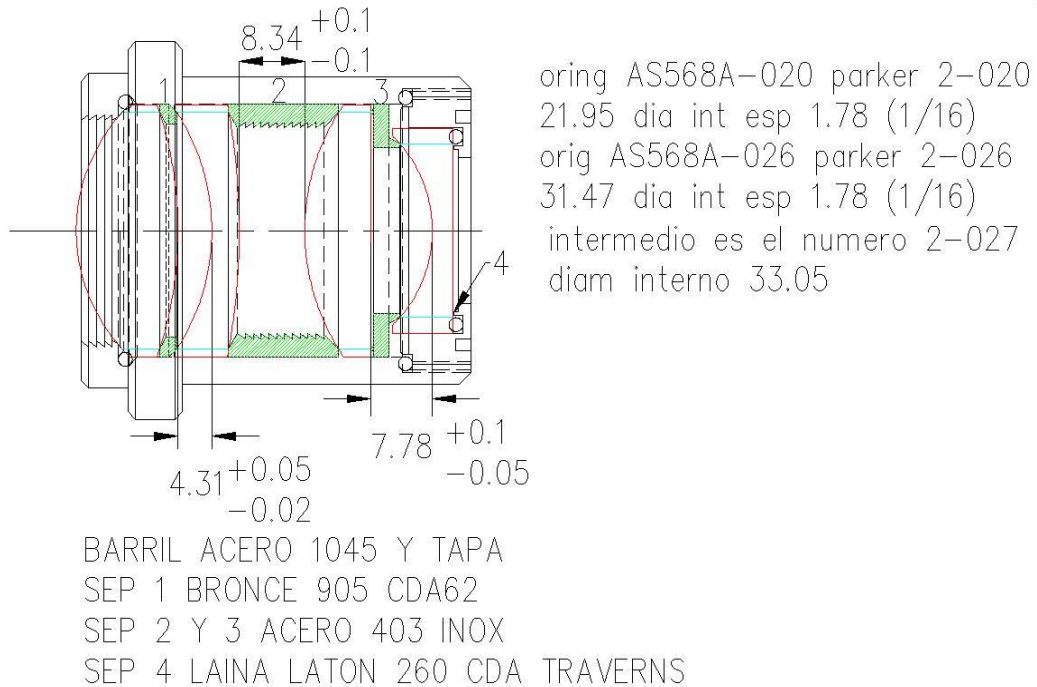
Barril de la cámara ensamblado con sus tolerancias de posición
